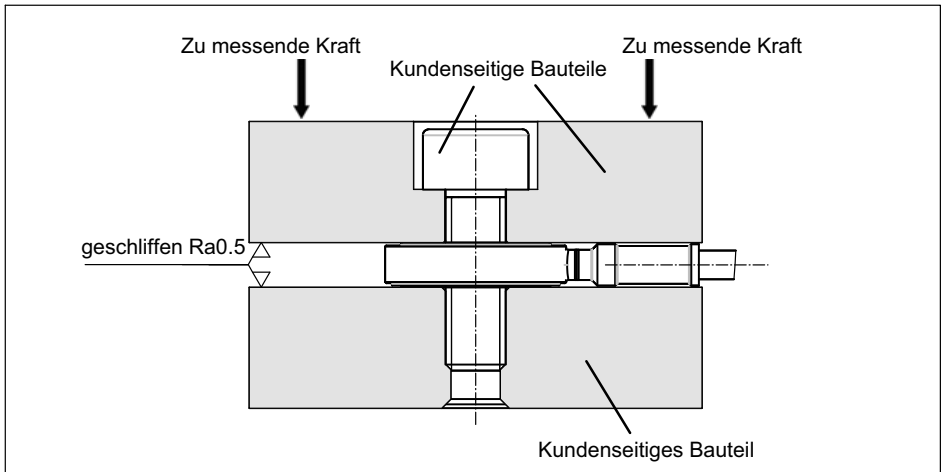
Kraftmessring mit Vorspannung durch Schraube
